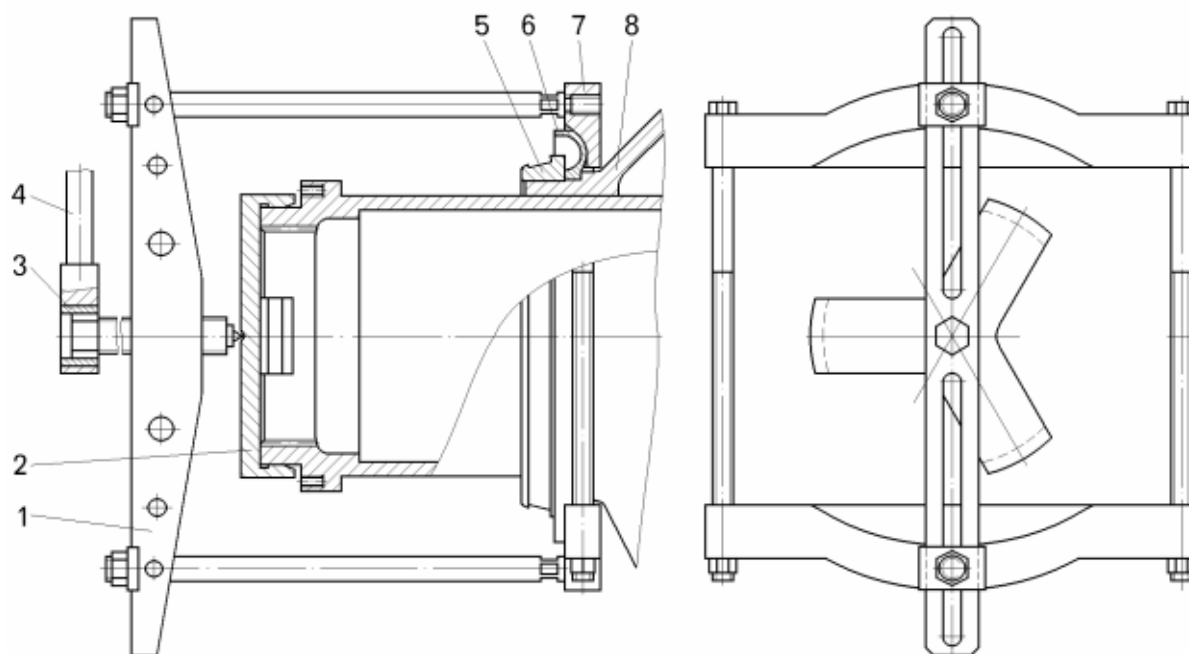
Приспособление для снятия внутреннего кольца внутреннего подшипника вместе с внутренней крышкой передней ступицы:
